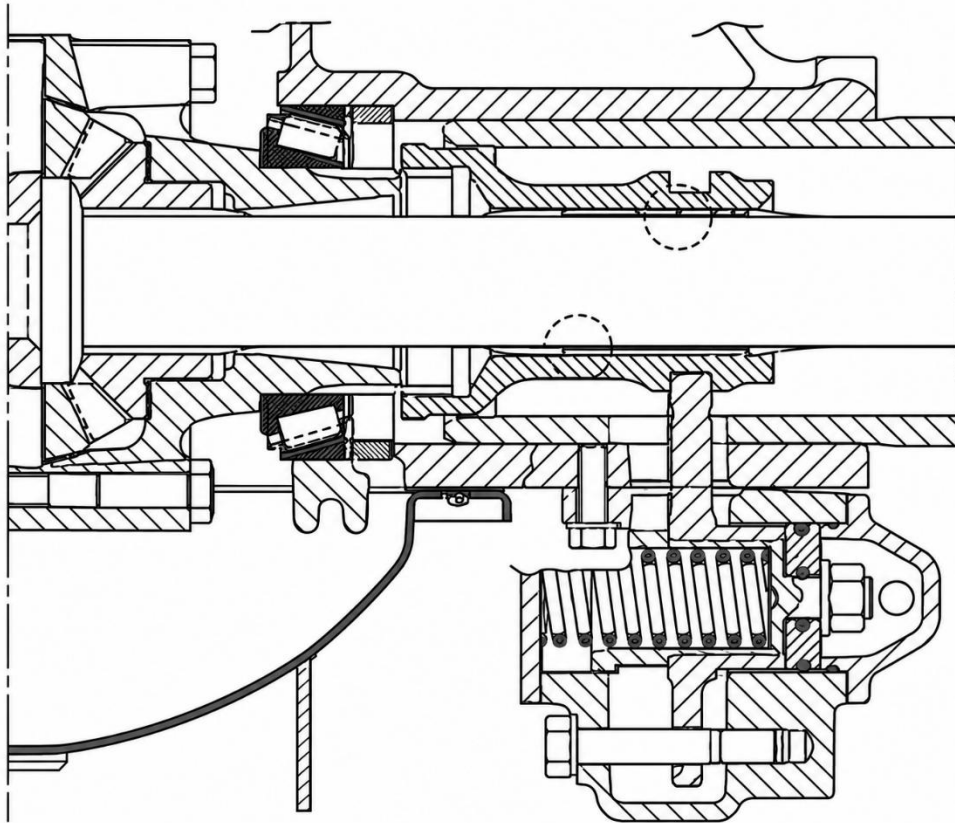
Розріз приводу механізму блокування диференціала.
